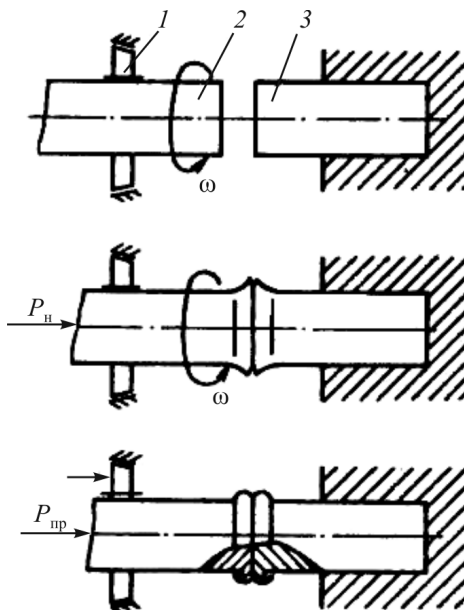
Схема сварки трением с непрерывным приводом: 1 – тормоз; 2, 3 – свариваемые заготовки;  $P_n$  – удельное давление при нагреве;  $P_{пр}$  – удельное давление проковки
